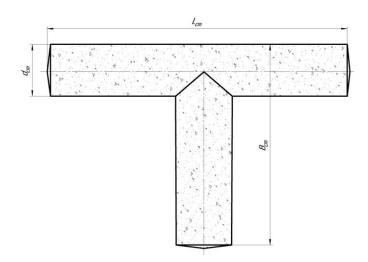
Эскиз стержня для формования отверстия в отливке
